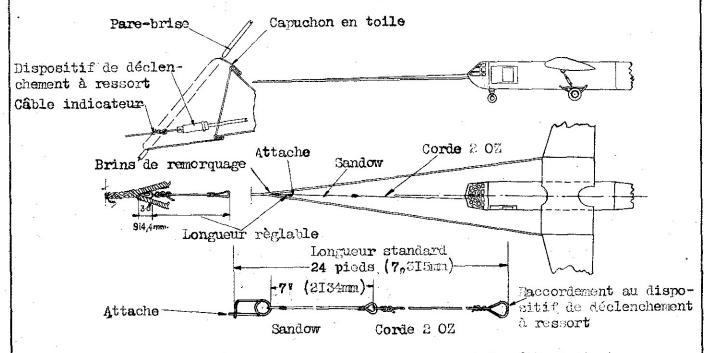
Ensemble général des cordes de remorquage et du câble indicateur.
